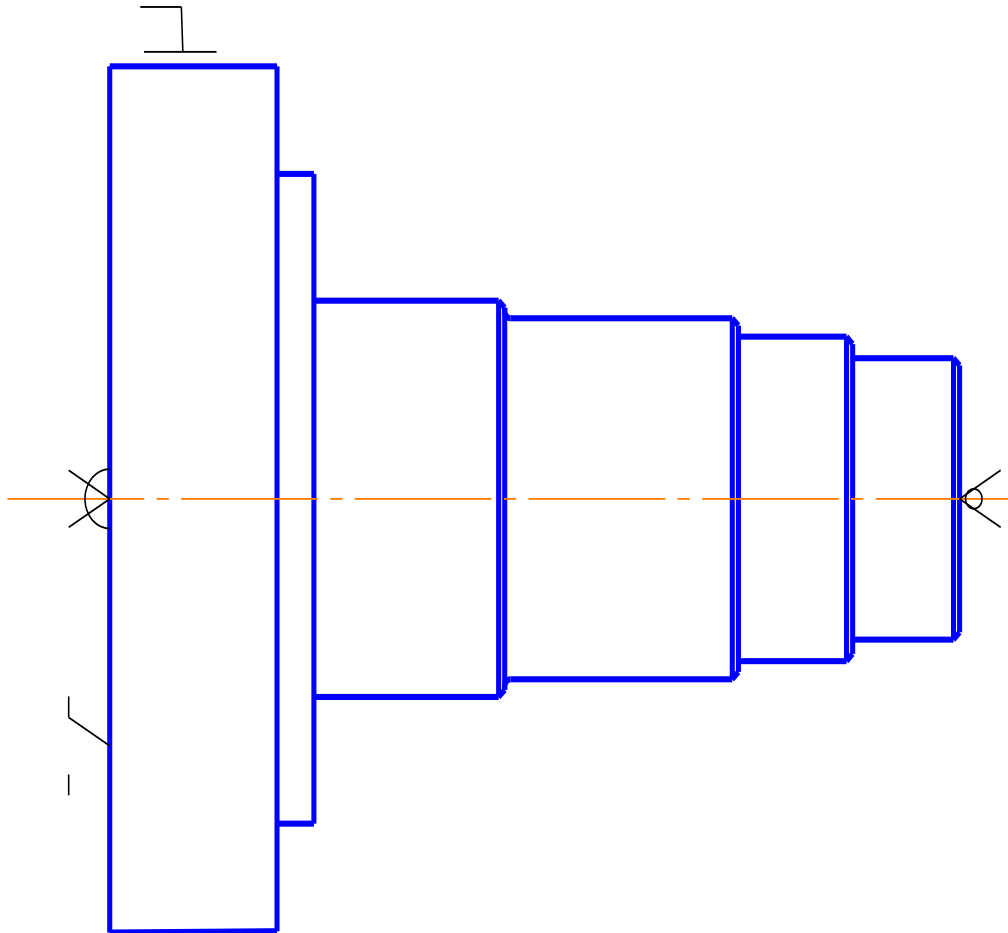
Эскиз базирования детали на токарной операции
